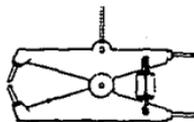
Equipo de soldadura con tenazas articuladas.
